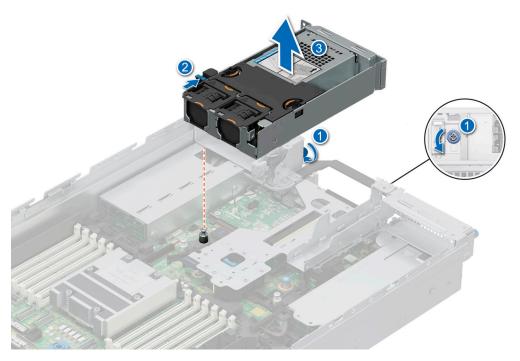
Entfernen des hinteren Laufwerksmoduls für 2 x 2,5"
